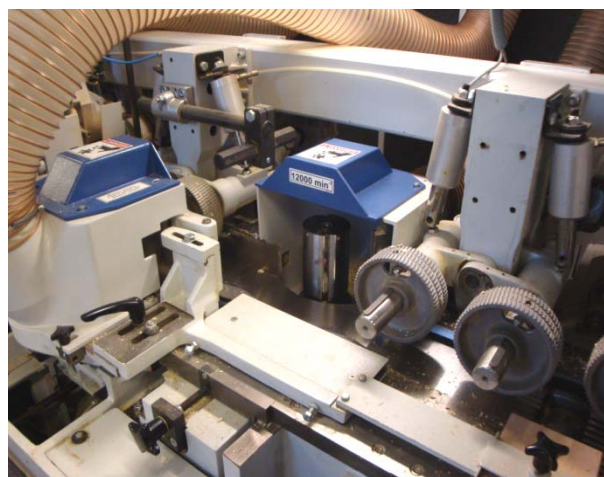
Внешний вид привода правого вертикального фрезерного шпинделя станка Unimat 23 EL
